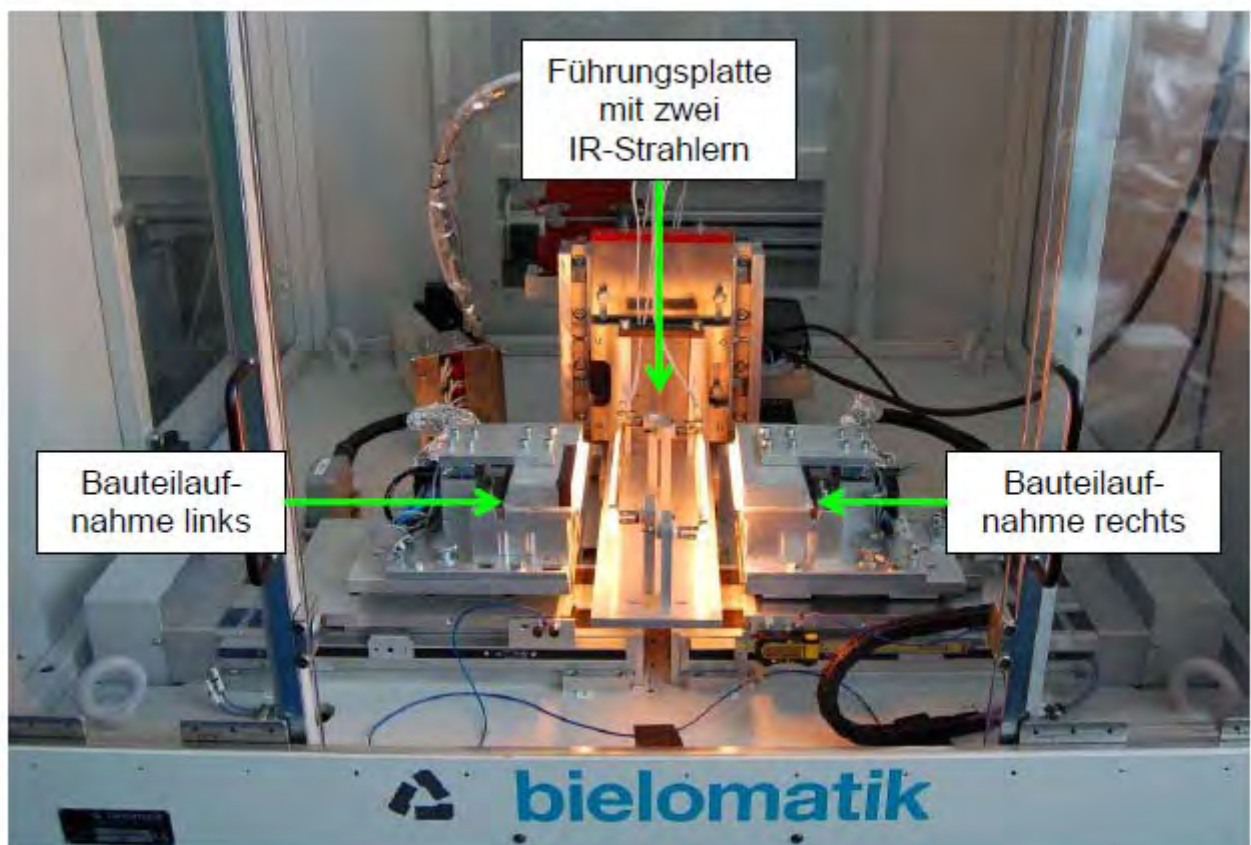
Schweißmaschine für Aufschmelz- und Schweißversuche
